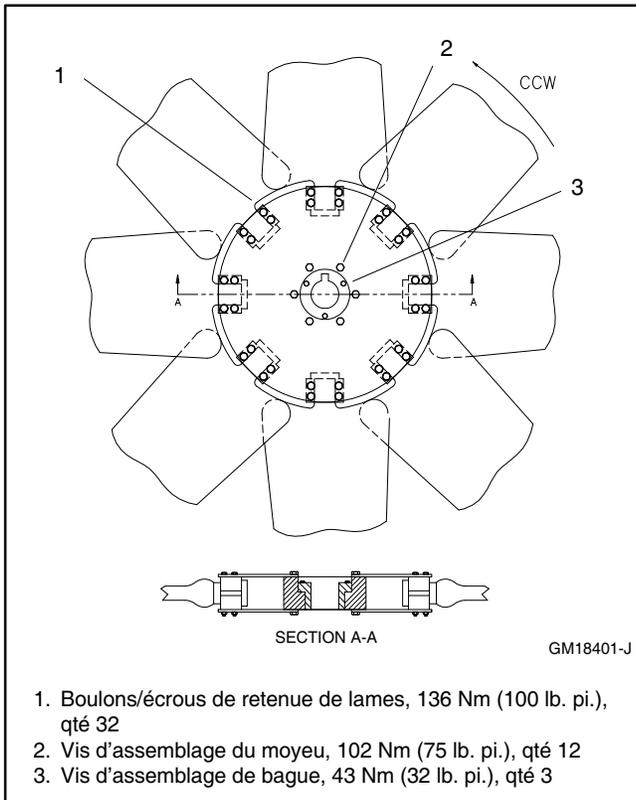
Emplacement de la quincaillerie du ventilateur et serrage
